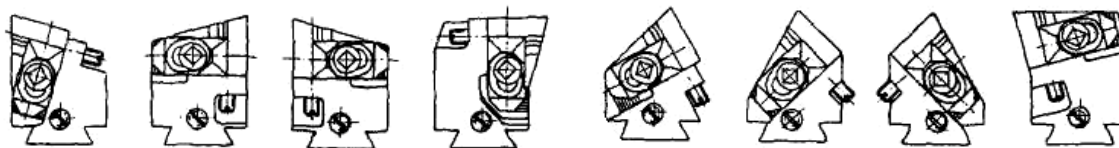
Резцовые блоки с креплением режущих пластин без отверстия
